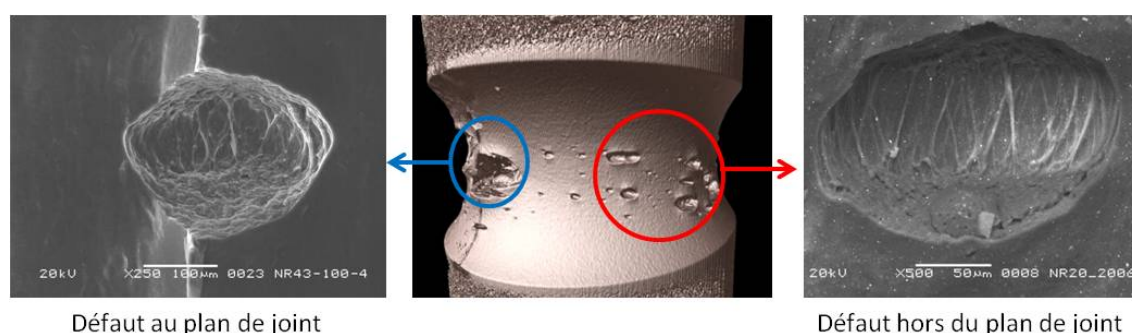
Vue d'ensemble des fissures de fatigue et images MEB de défaut au plan de joint et hors plan de joint.
